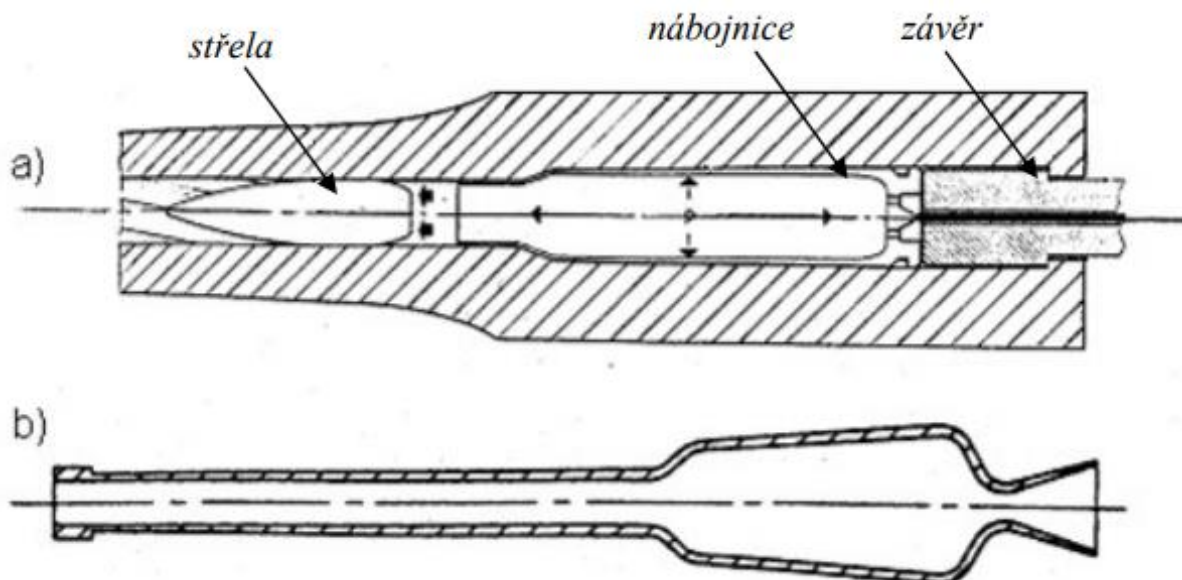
Řez nábojem 9 mm Luger – podle [9].
